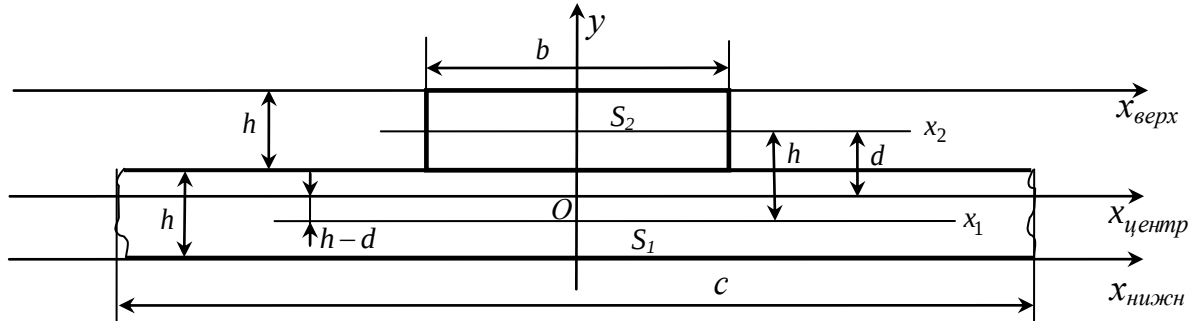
Схема соединительного шва, расположенного с лицевой стороны изделия
